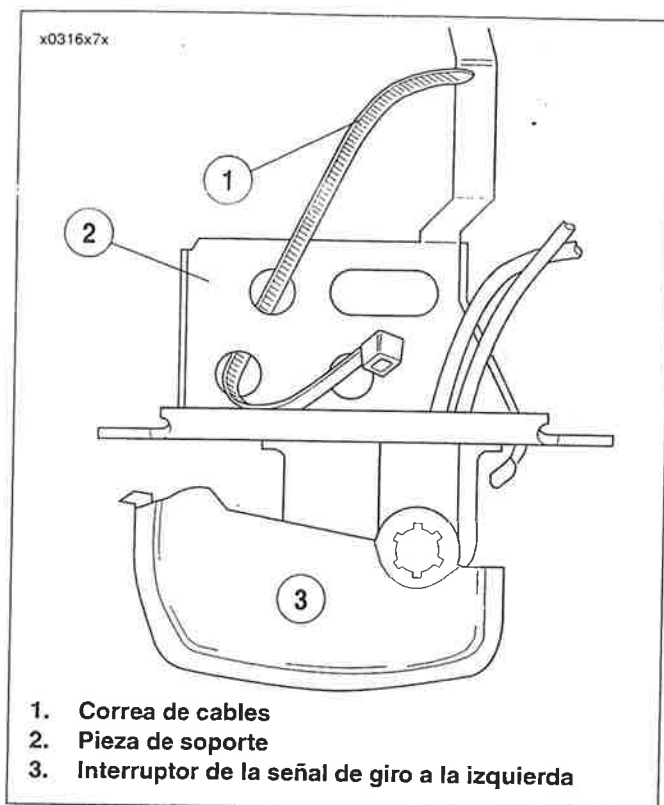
Insertar la correa de cables en la pieza de soporte del interruptor
